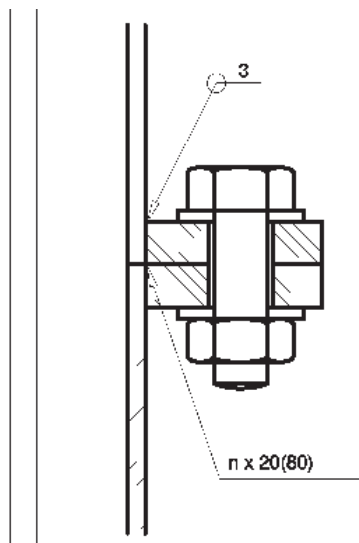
Flanschverbindung mit Flansche, geschweißt.
